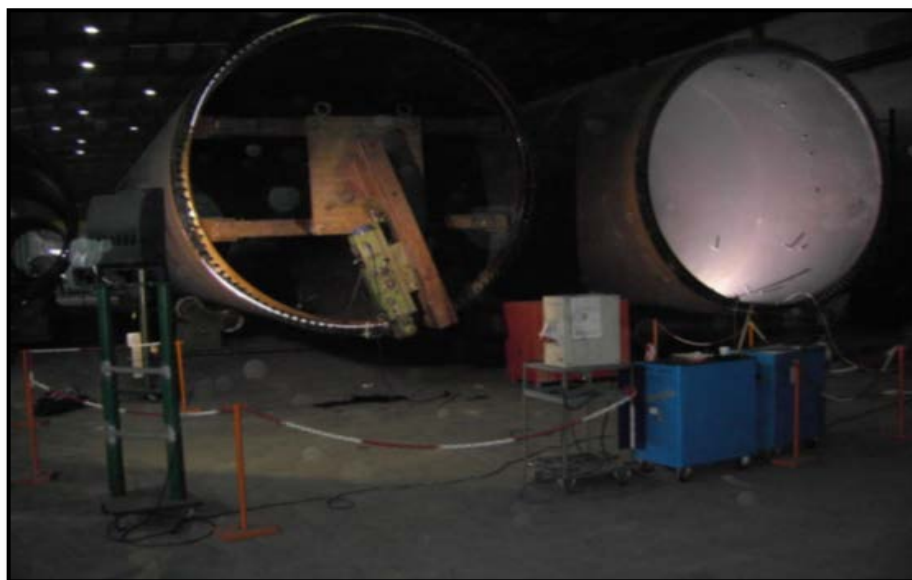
Ajuste posicional de uma flange por maquinagem.
